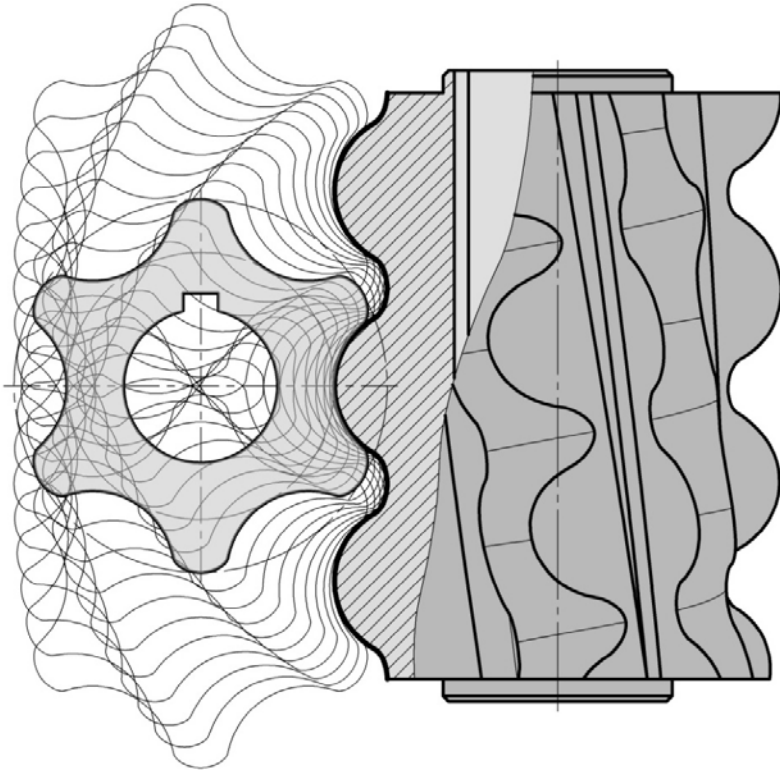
Схема утворення профілю черв'ячної фрези для обробки ротора героторної передачі
